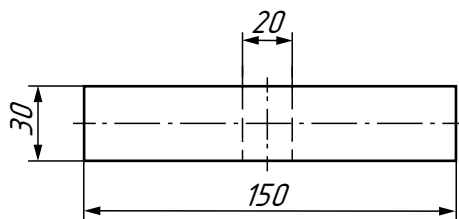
Чертёж детали из древесины с отверстием (вид спереди)
